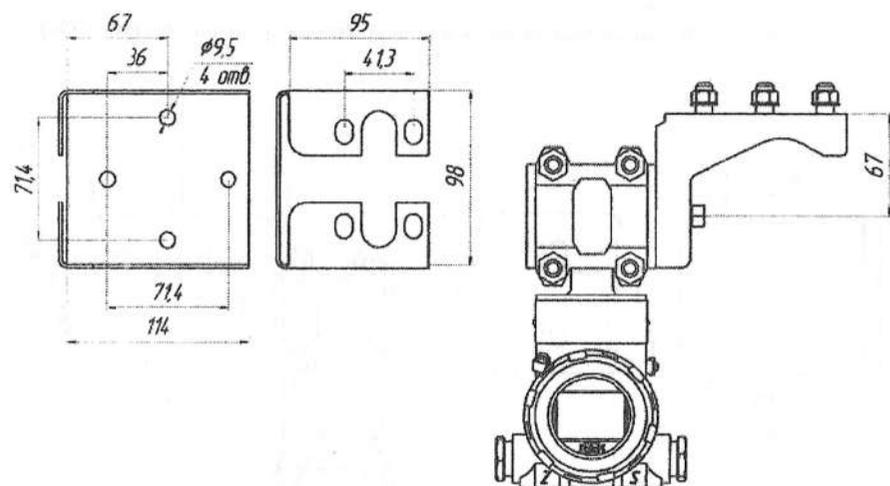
Угловой кронштейн для крепления на панели (B05), габаритные и присоединительные размеры
